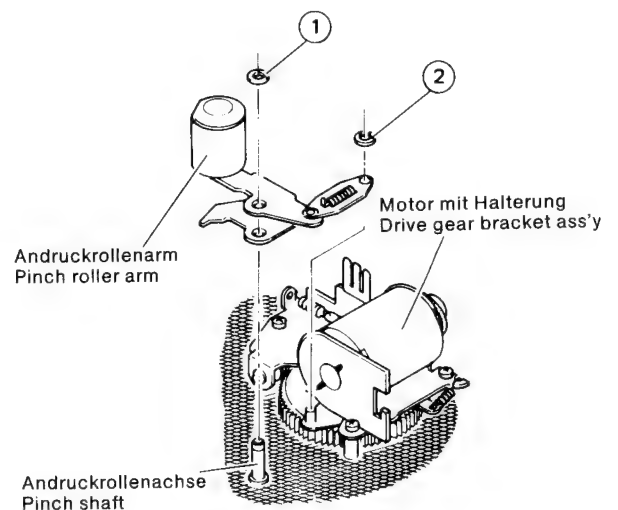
Ausbau der Andruckrolle /
